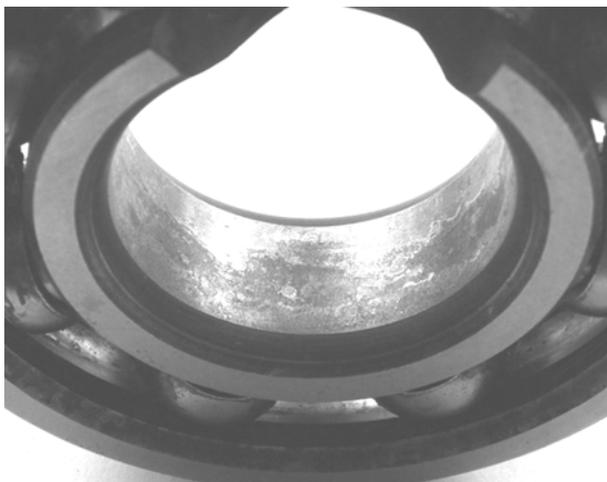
Следы фреттинг-коррозии на посадочной поверхности внутреннего кольца шарикоподшипника
